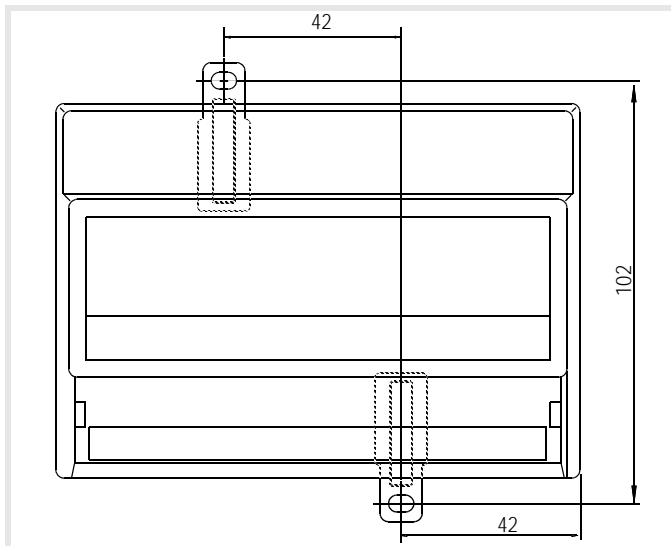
Maßzeichnung für Wandmontage (Frontansicht)
